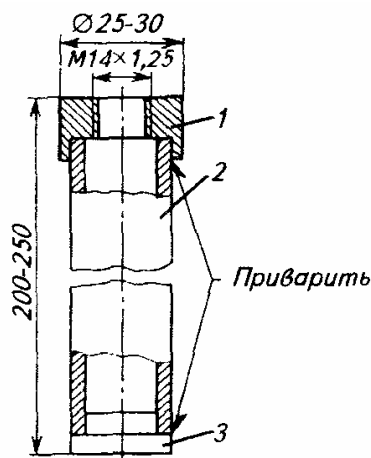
Приспособление для очистки свечей зажигания: 1 – втулка с резьбой под свечу; 2 - трубка; 3 - заглушка
